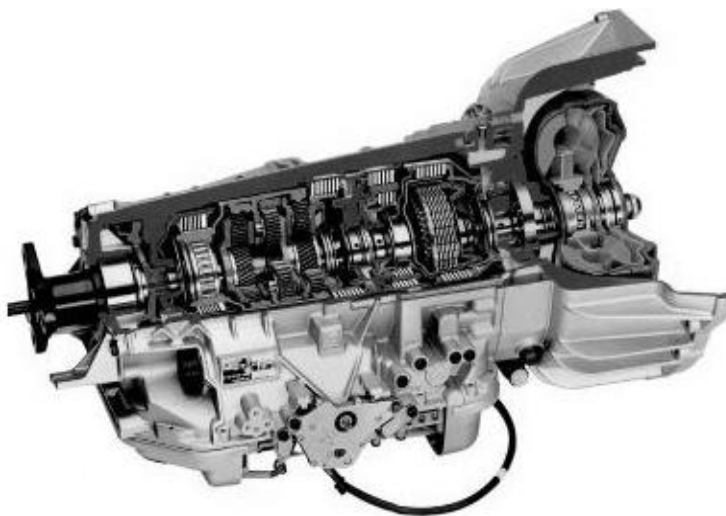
Гидромеханическая коробка передач заднеприводного
